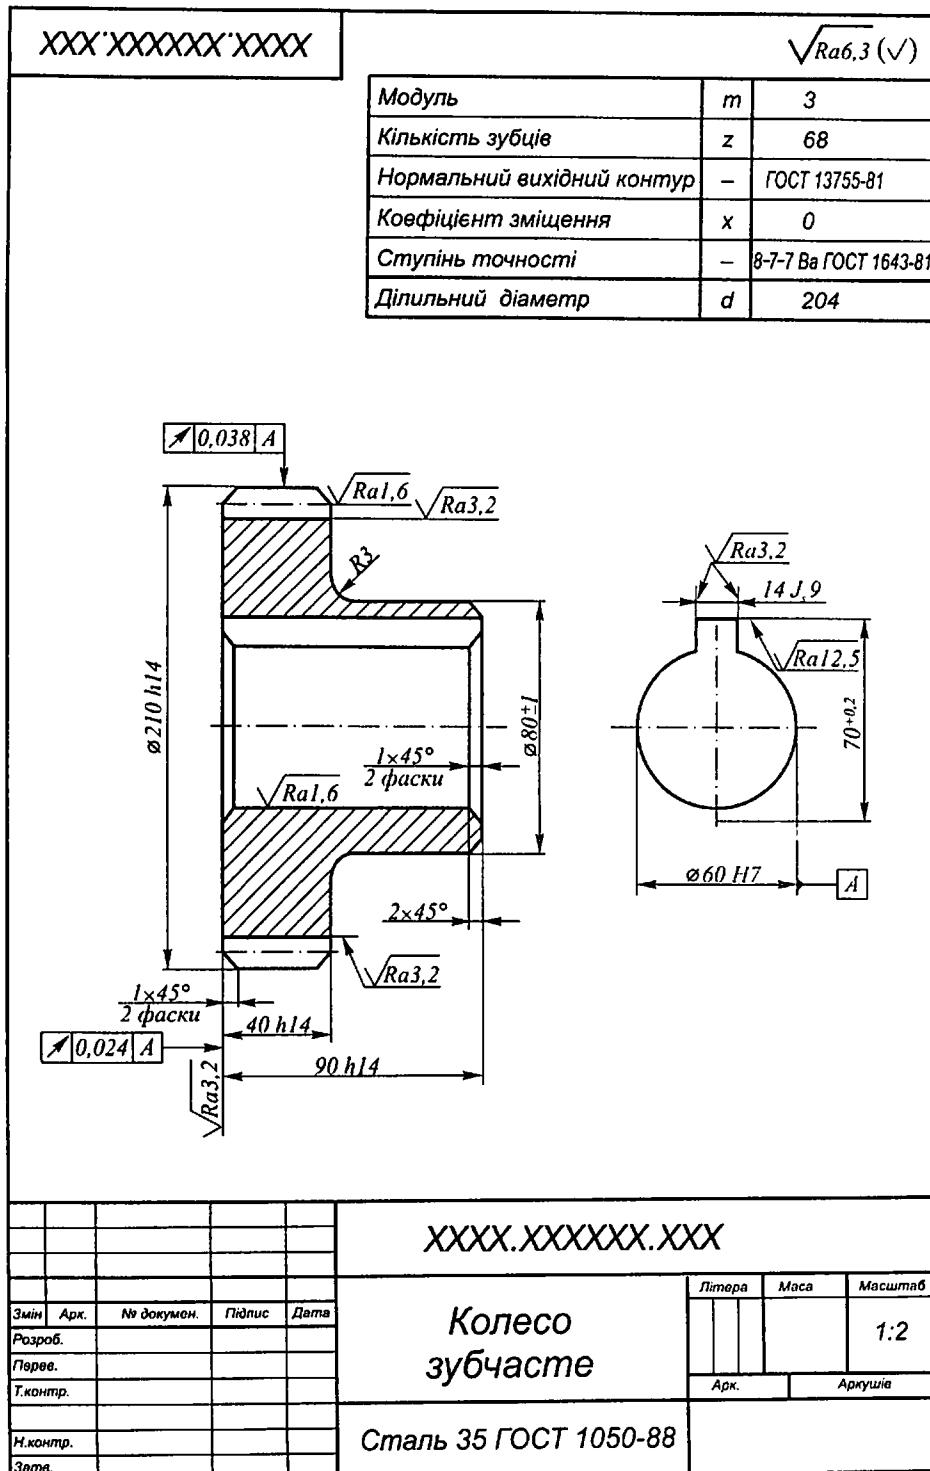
Приклад виконання кресленика циліндричного зубчастого колеса
